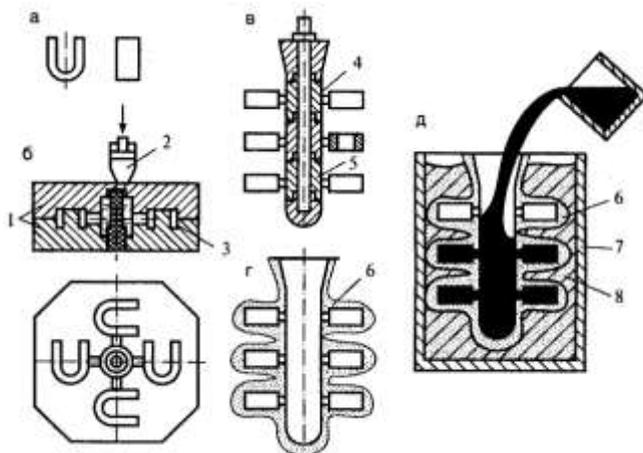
Литье по выплавляемым моделям: а – деталь; б – изготовление блока моделей; в – сборка блоков; г – нанесение покрытия; д – заливка формы. 1 – пресс-форма; 2 – шприц; 3 – модельная композиция; 4 – блок; 5 – металлический стержень; б – оболочковая форма; 7 – опока; 8 – песок
